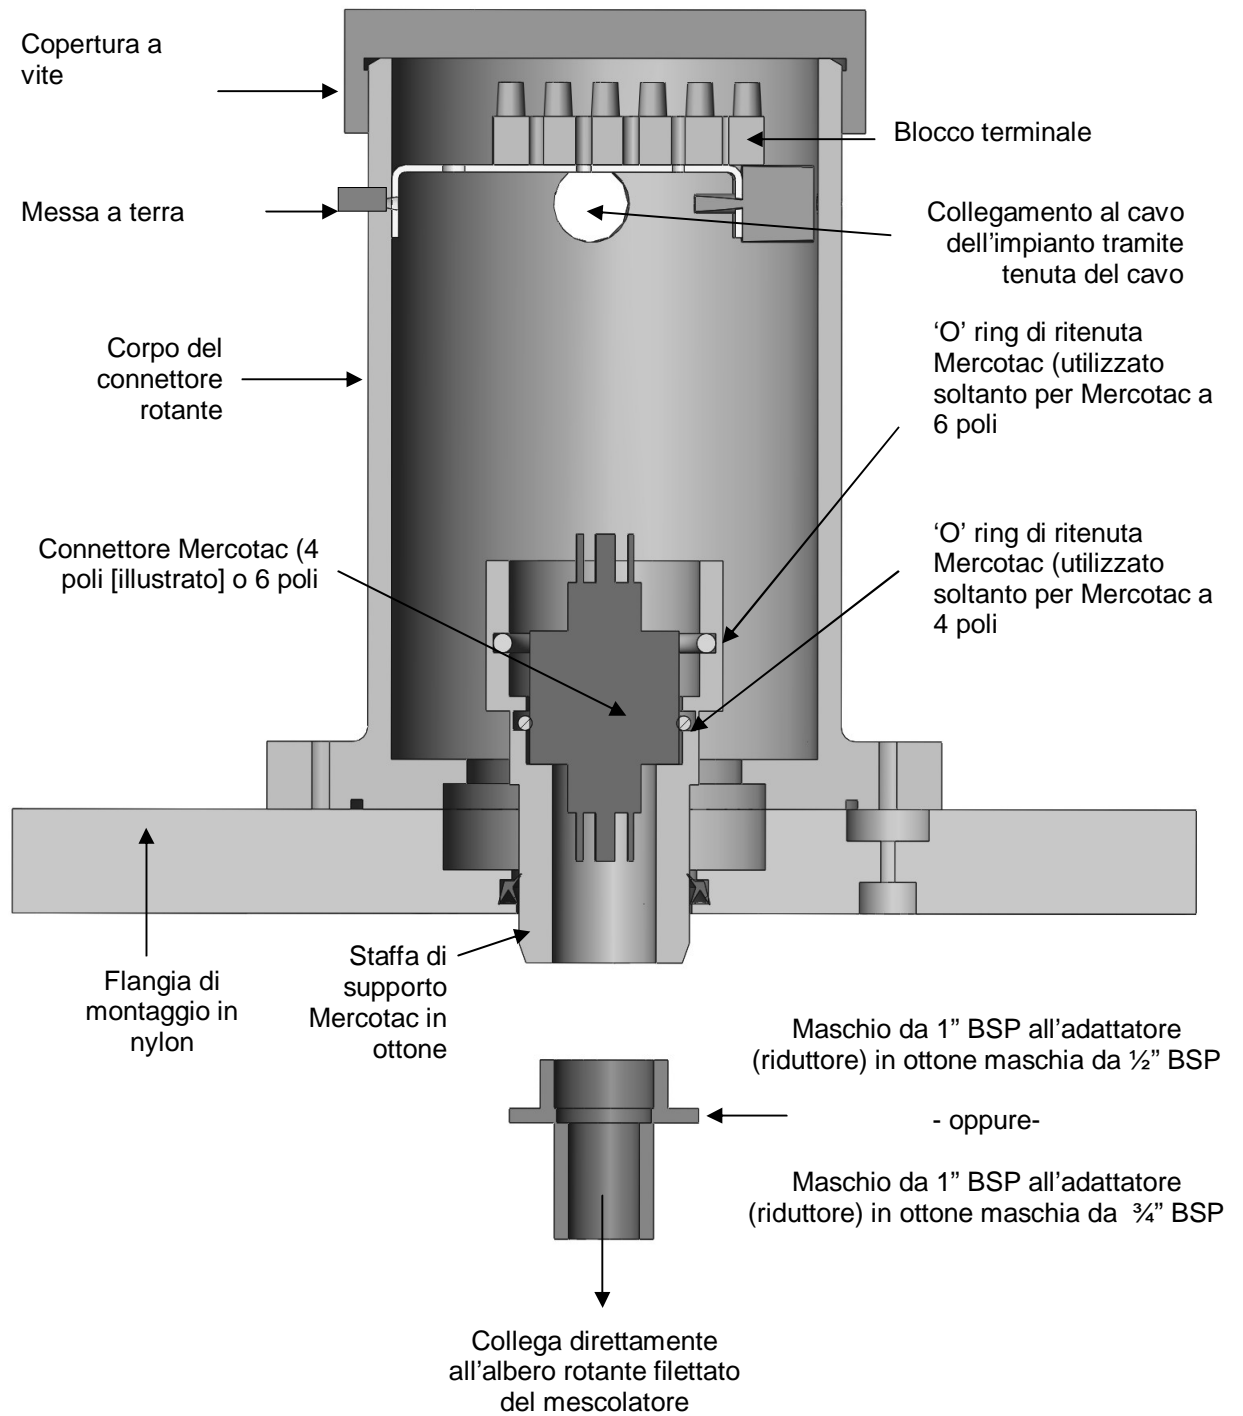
Tipo 'A': assemblaggio del connettore rotante
